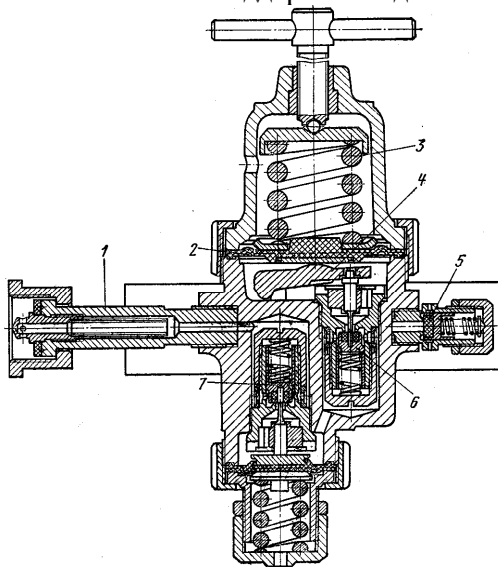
Двухкамерный кислородный редуктор ДКД-8-65:
